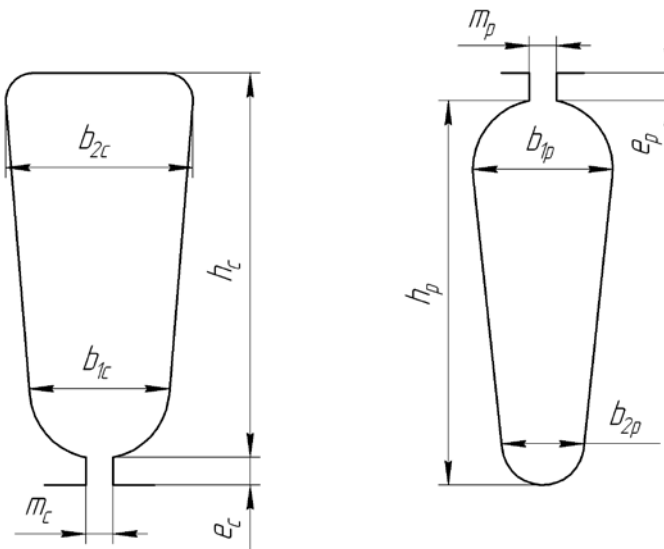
Форма пазов статора и ротора исследуемого двигателя
